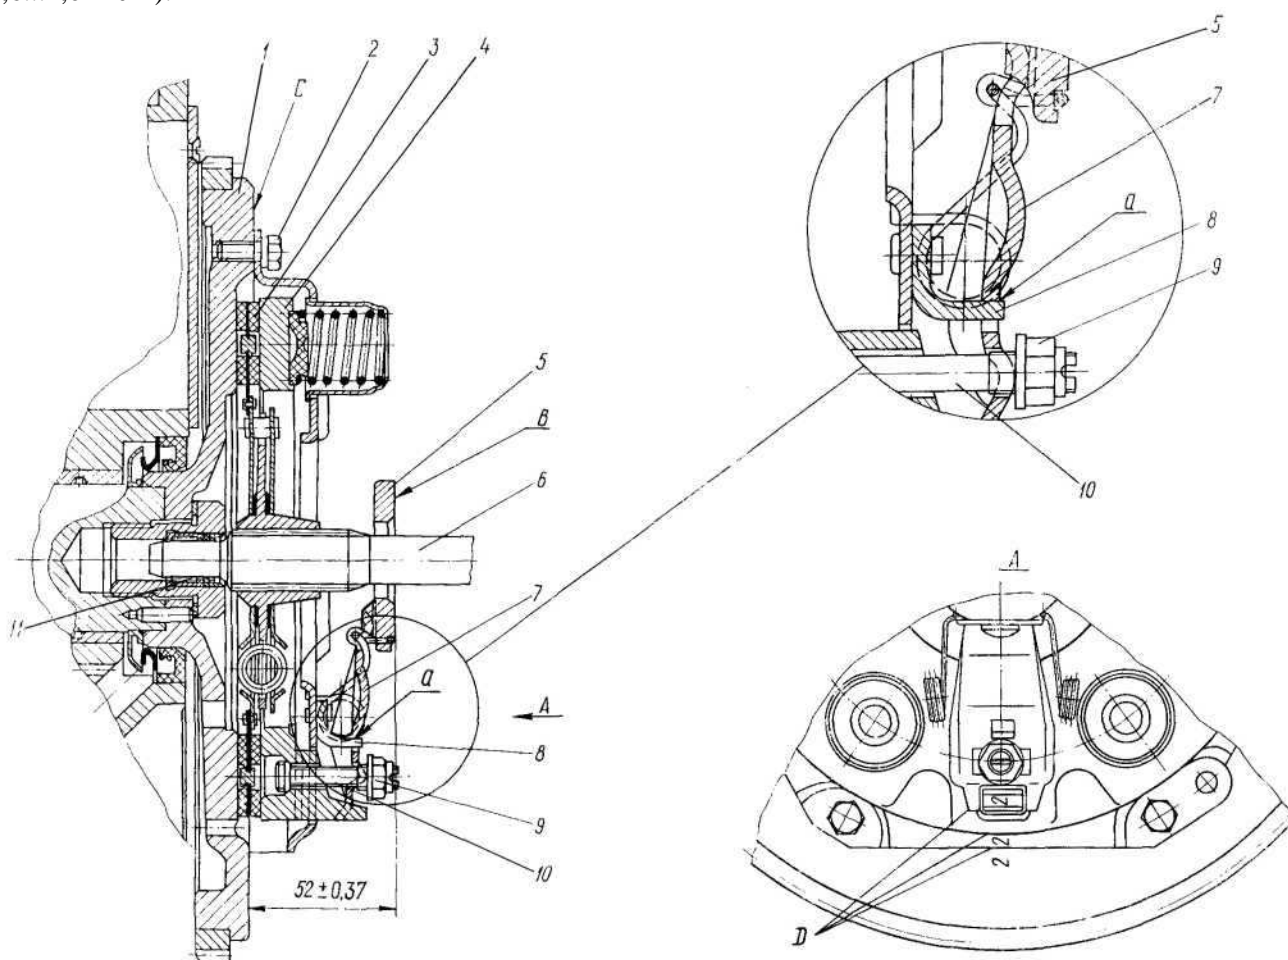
Установка ведомого диска сцепления с помощью оправки:
